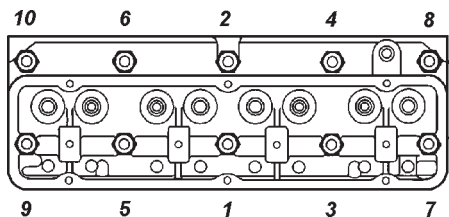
Порядок подтяжки гаек головки блока цилиндров
